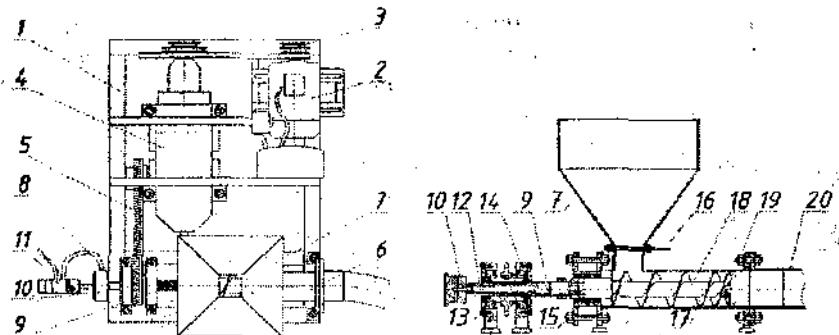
Шнековий пневмо-механічний транспортер (креслення):
